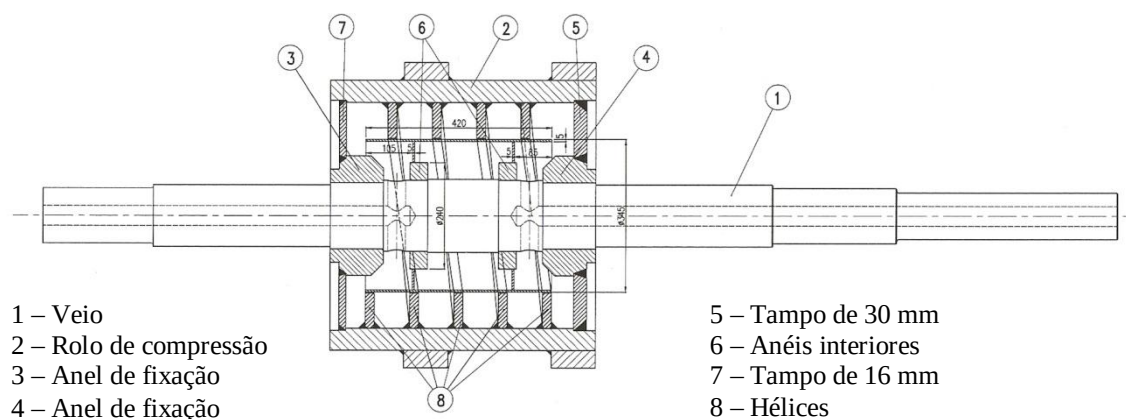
Corte longitudinal do conjunto do rotor
